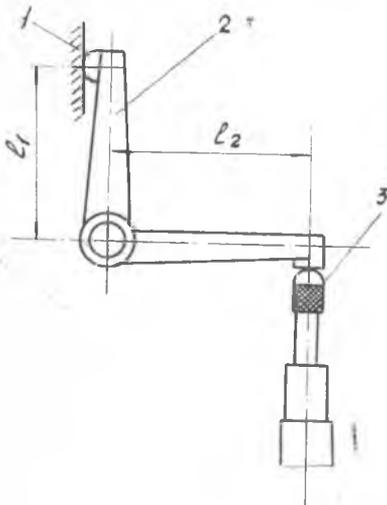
Рычажные передаточные устройства: 1 — проверяемая деталь; 2 — рычаг; 3 — измерительный прибор
